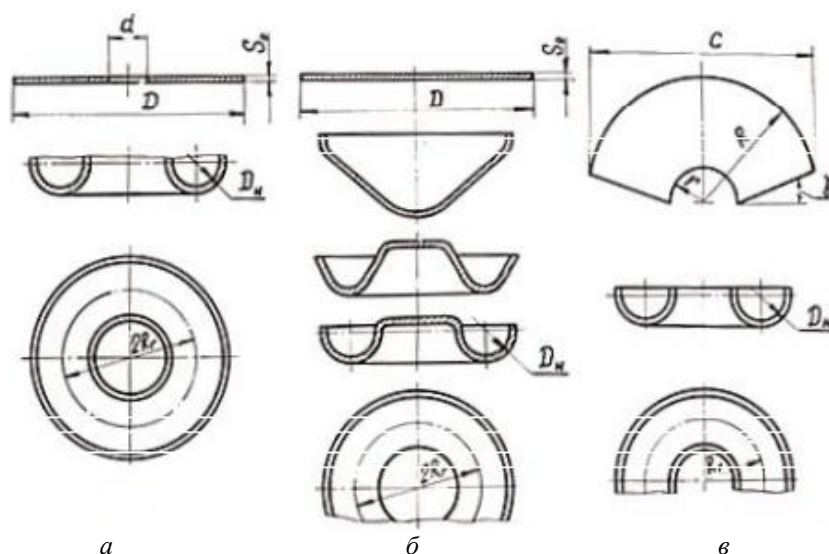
Способы штамповки полуторов и отводов из листовых заготовок:
